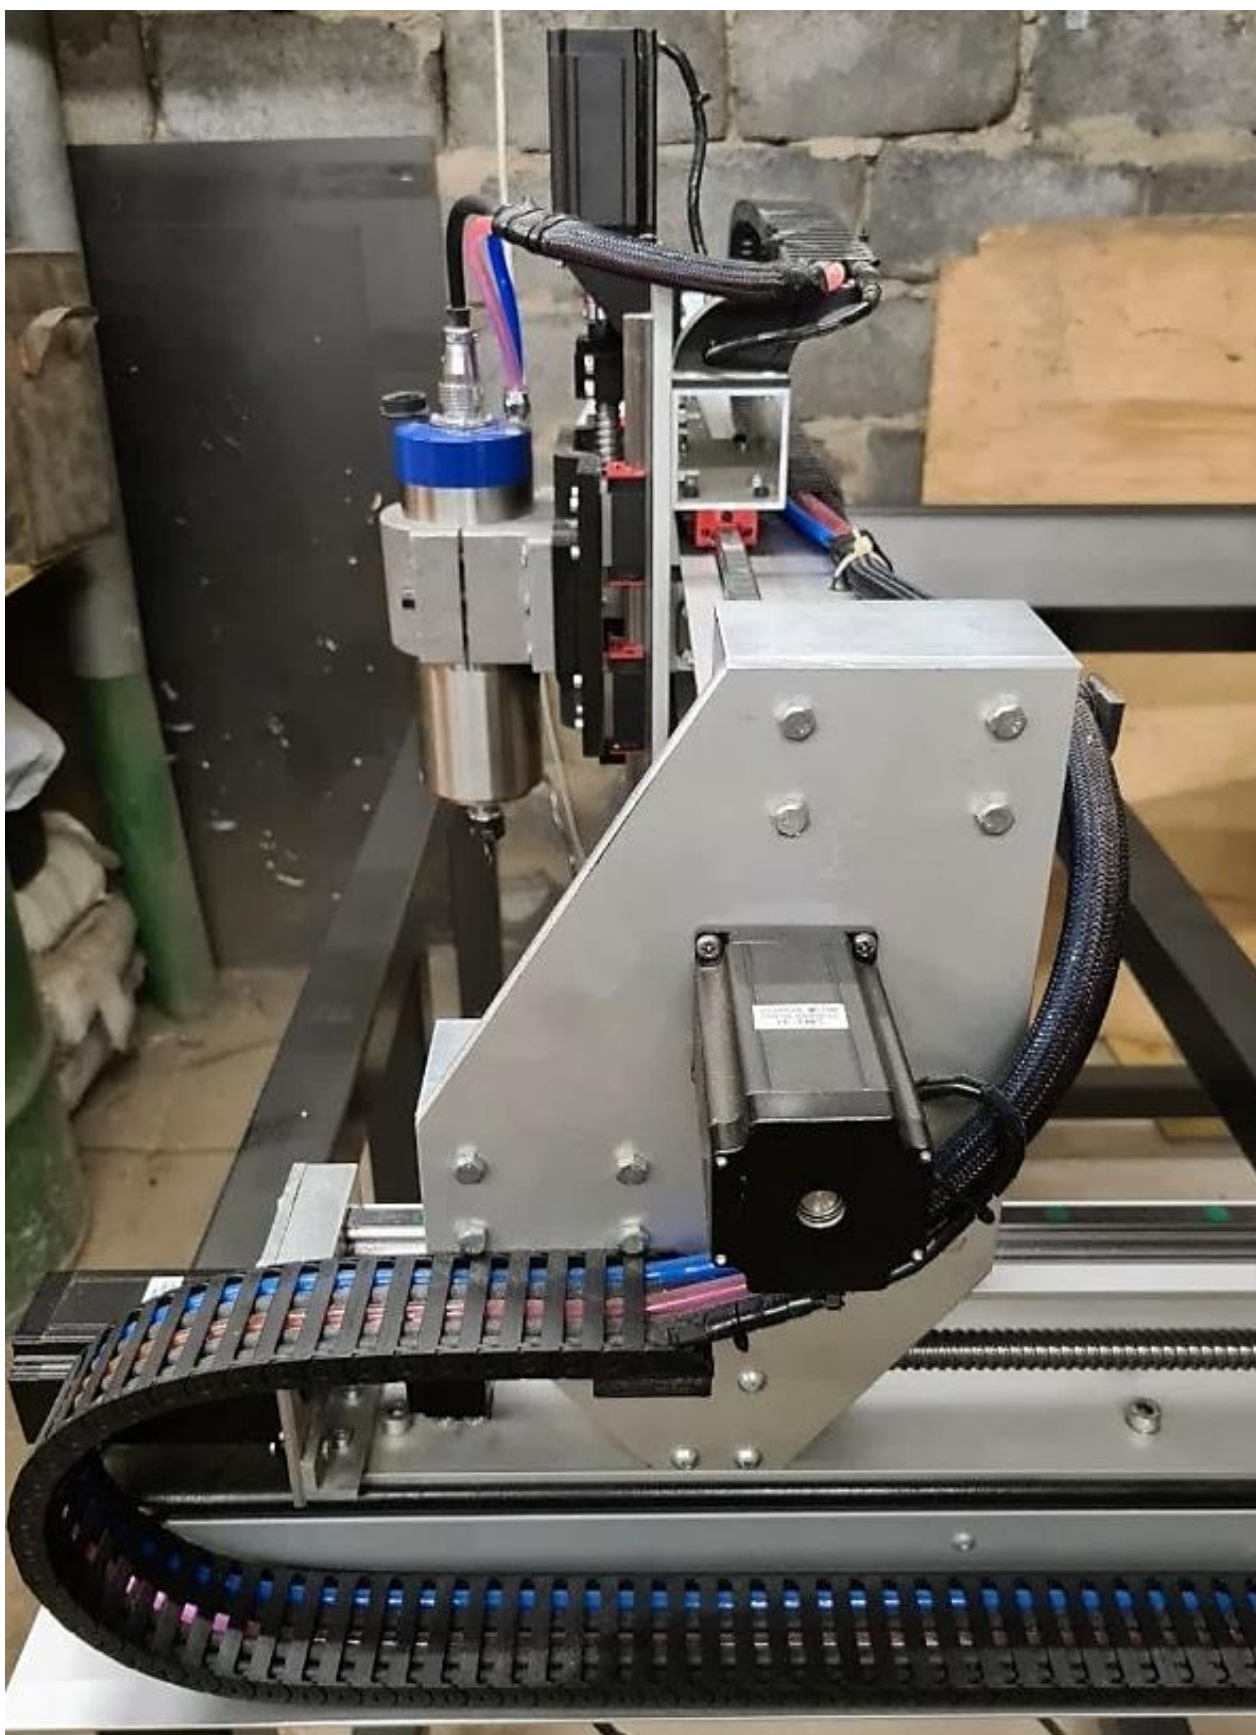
Зібраний макет фрезерного верстату з ЧПК, вид збоку
